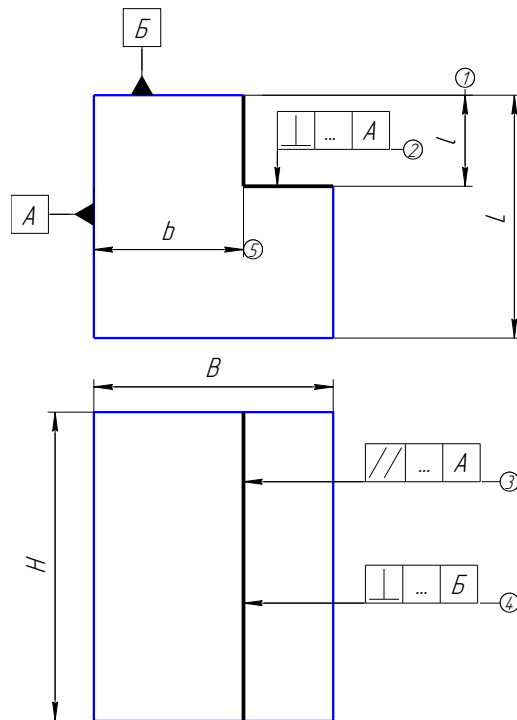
Ескіз оброблюваної деталі з технічними вимогами до операції фрезерування уступу
